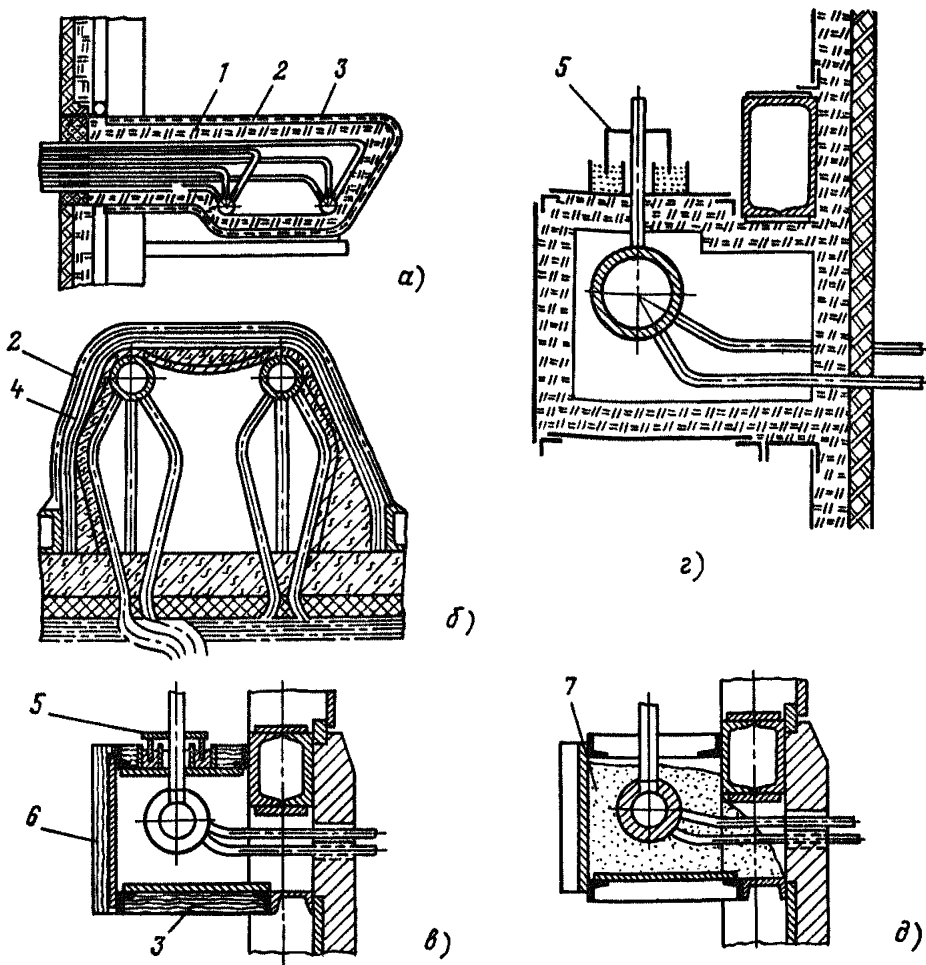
Конструкции уплотнений прохода труб пароперегревателя и водяного экономайзера.
